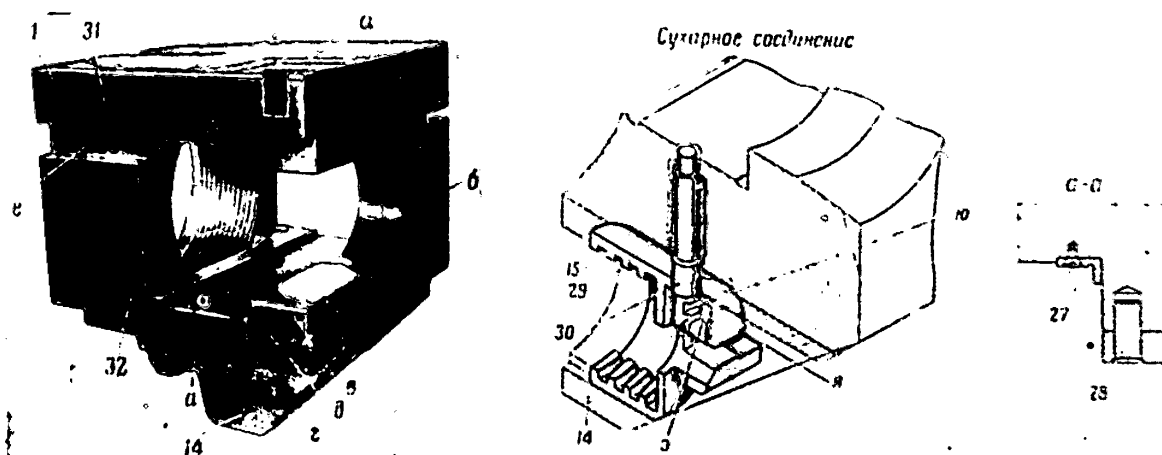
Казеппик (вид слева сверху) и сутарное соединение:
